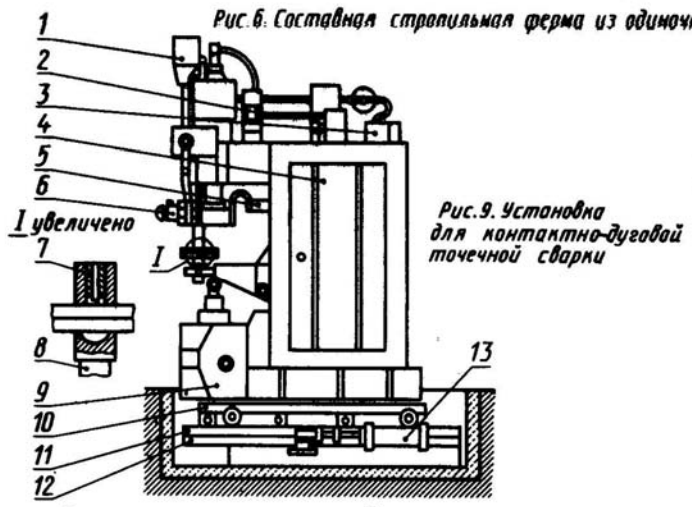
Установка для контактно-дуговой точечной сварки
